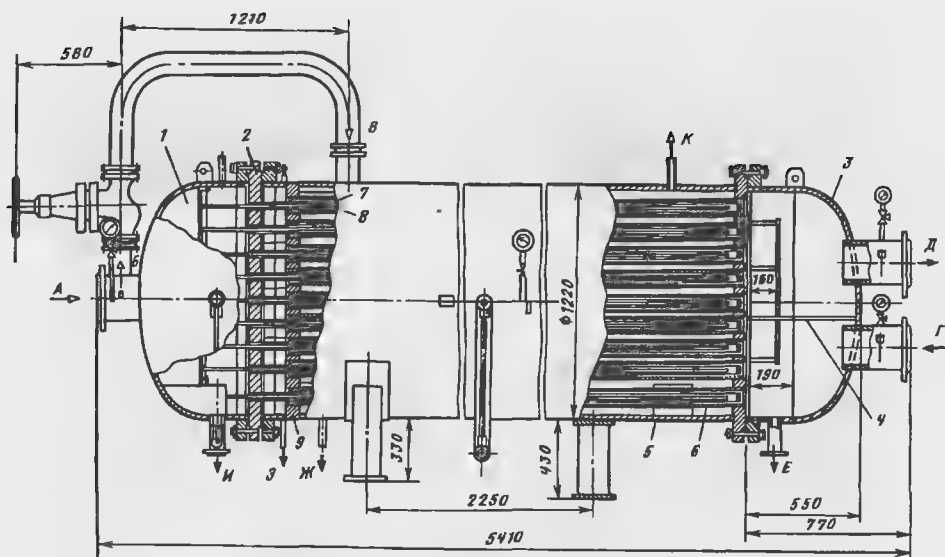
Общий вид подогревателя марки ПМР-13-120; 1 – паровая камера, 2 – трубная доска паровой камеры; 3 – мазутная камера; 4 – перегородка мазутной камеры; 5 – блок-корпус аппарата; 6 – наружная труба нагревательных элементов; 7 – внутренняя продольно-ребренчатая труба нагревательных элементов; 8 – дополнительная паровая труба; 9 – трубная доска блока-корпуса; А – вход пара; В – отвод пара; В – выход пара; Г, Д – вход и выход мазута; Е, З – дренажи мазута; Ж, И – отвод конденсата; К – отсос воздуха
